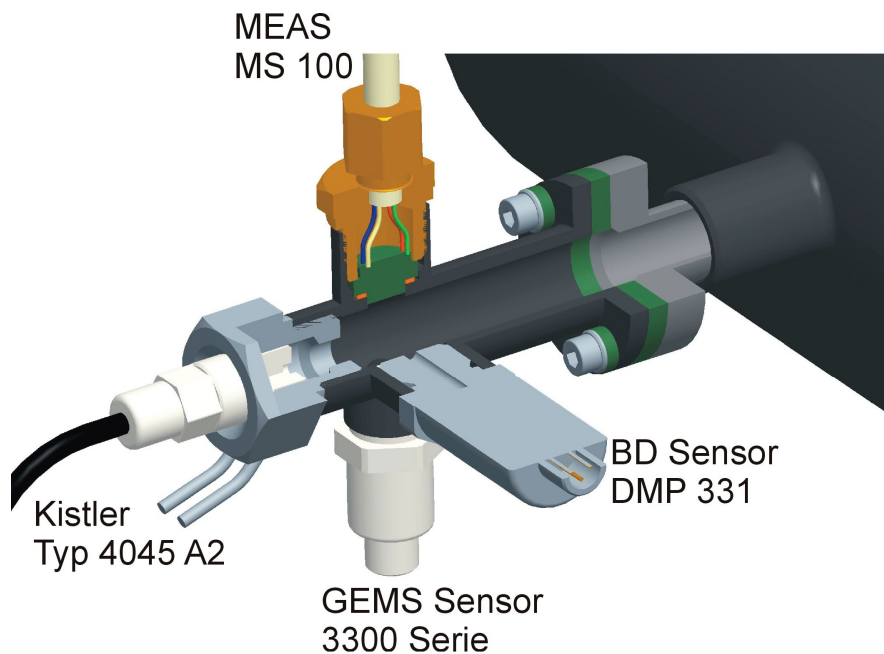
Prinzipskizze des Adapterflansches für insgesamt 4 Drucksensoren
